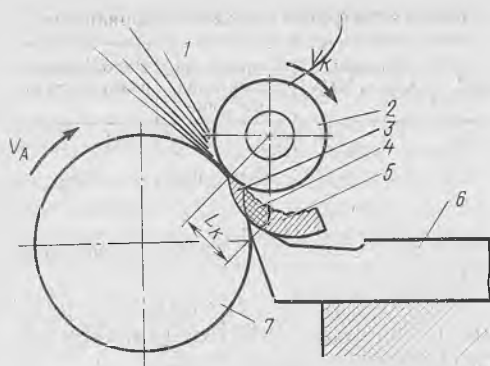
Схема абразивно-лезвийного способа обработки:
